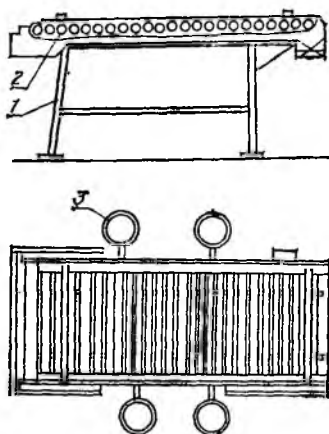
Роликовый переборочный стол конструкции ГДР:
